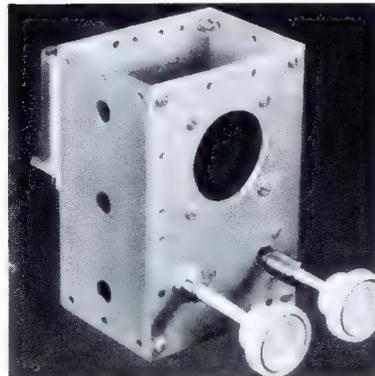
Die Lautsprecherseite des Chassis mit den Drehknöpfen
